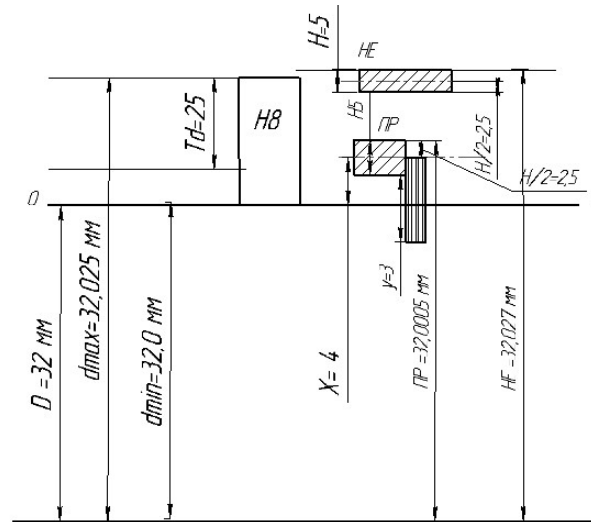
Схема розташування полів допусків для розміру  $\varnothing 32H8$
